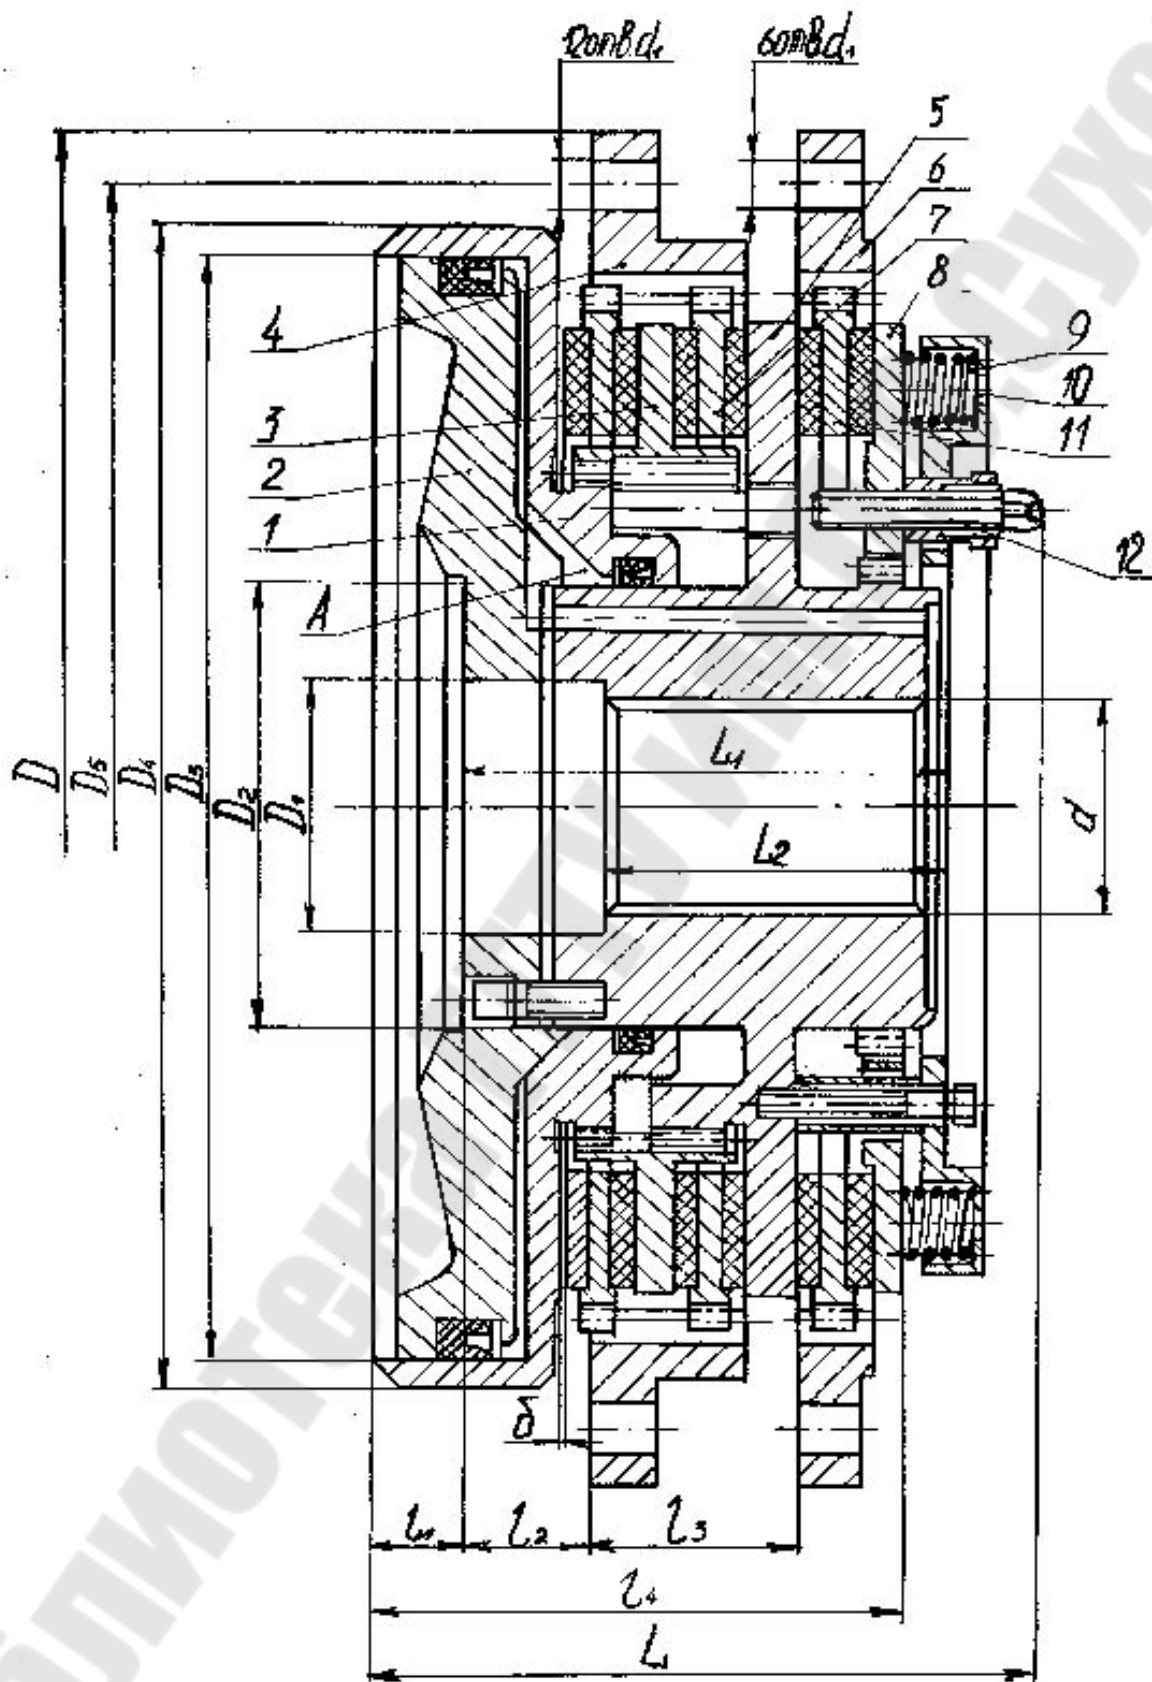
Габаритные и присоединительные размеры муфты тормоза фрикционного типа УЗ...
